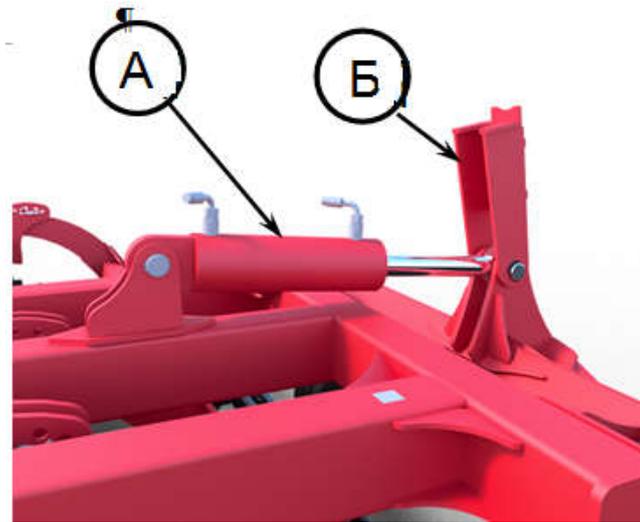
Гідроциліндр транспортного пристрою і транспортний упор в робочому положенні:
